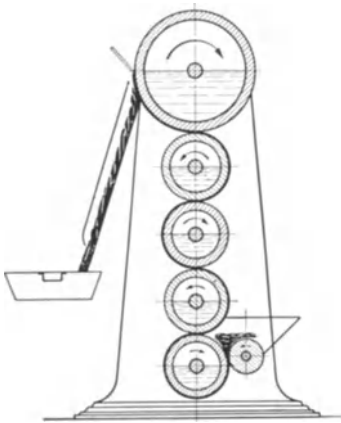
Schnittzeichnung eines älteren Schokoladenwalzenstuhls mit einer geriffelten Auftragwalze und 5 wassergekühlten Stahlwalzen. Die Umdrehungsrichtung und Umfangsgeschwindigkeit ist durch Pfeile entsprechender Länge gekennzeichnet. Der Weg der Schokoladenmasse ist durch eine schwarze Linie angegeben. Oben links nimmt ein Abstreichmesser die Masse ab.
